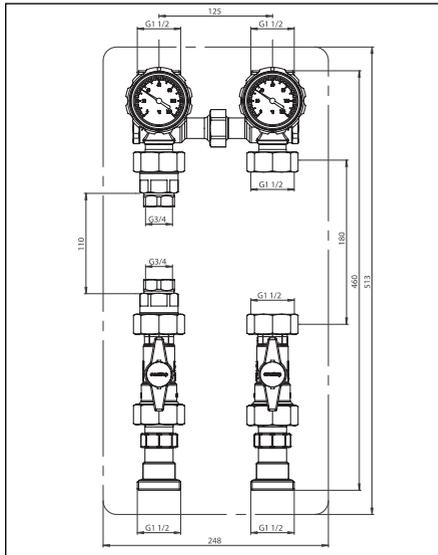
Abmessungen für Wärmemengenzähler 110 mm
